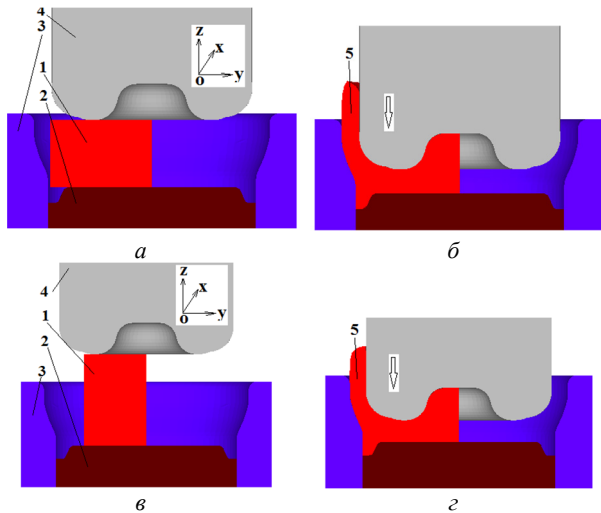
Розрахункові схеми на початку і в кінці видавлювання: *a* і *б* – циліндричної заготовки; *в* і *г* – заготовки квадратного перерізу
